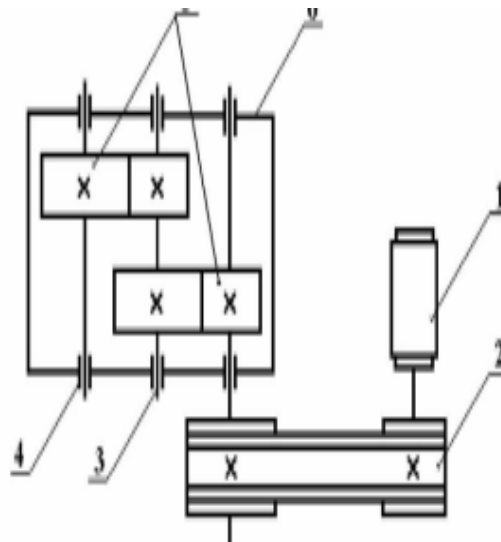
Кинематическая схема привода с цилиндрическим зубчатым редуктором
